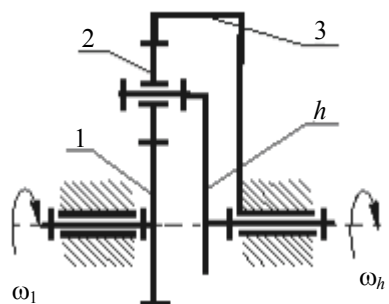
Кинематическая схема планетарного редуктора: 1 – шестерня; 2 – сателлит; 3 – эпицикл;  $h$  – водило
